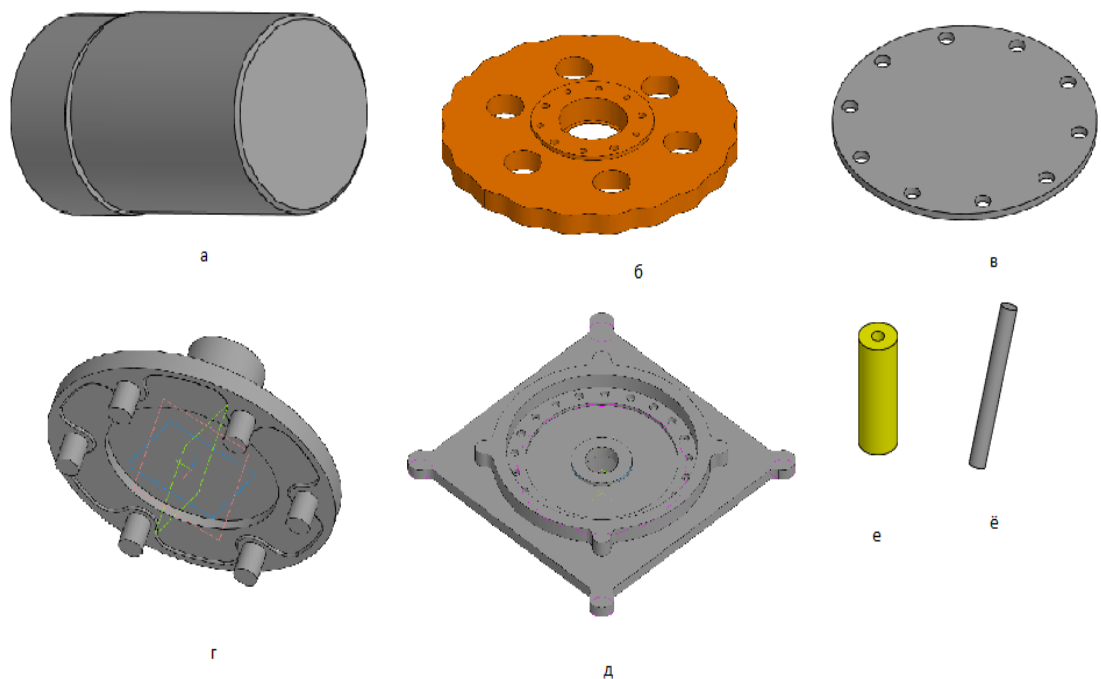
Твёрдые модели деталей циклоидного редуктора: а) вал с эксцентриком; б) циклоидное колесо; в) крышка вала; г) муфта (водило); д) корпус редуктора; е) ролик; з) ось ролика.
